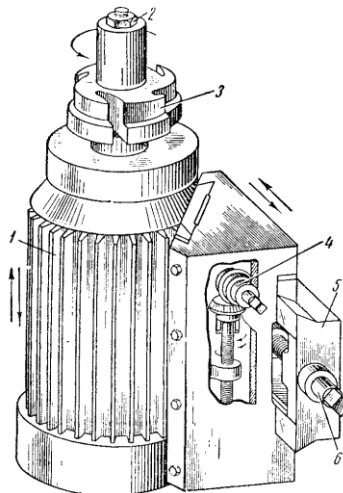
Електродвигун з валом, що служить одночасно вертикальним шпинделем стругального верстата: 1 — корпус, 2 — гайка, 3 — фреза, 4 — механізм підйому шпинделя, 5 — напрямного супорта; 6 — гвинт для переміщення шпинделя в горизонтальній площині
